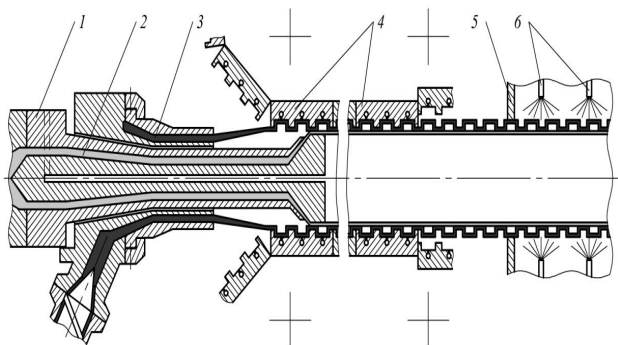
Схема виготовлення двошарових гофрованих полімерних труб: 1 – екструзійна головка; 2, 3 – трубні заготовки внутрішнього і зовнішнього шарів, відповідно; 4 – півформи гофратора; 5 – ванна охолодження; 6 – водяні форсунки.
